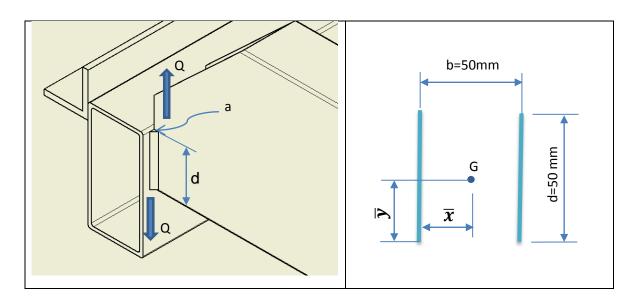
Esquema esfuerzo y distribución soldadura de filete
